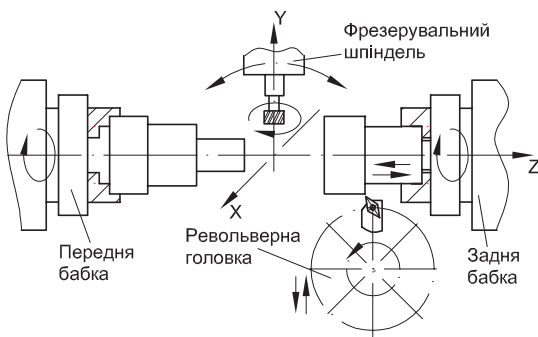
Схема токарно-фрезерного оброблювального центру
